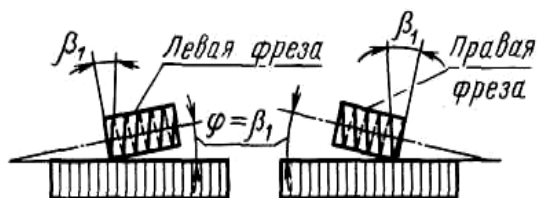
Расположение червячной фрезы при зубофрезеровании прямозубого колеса
